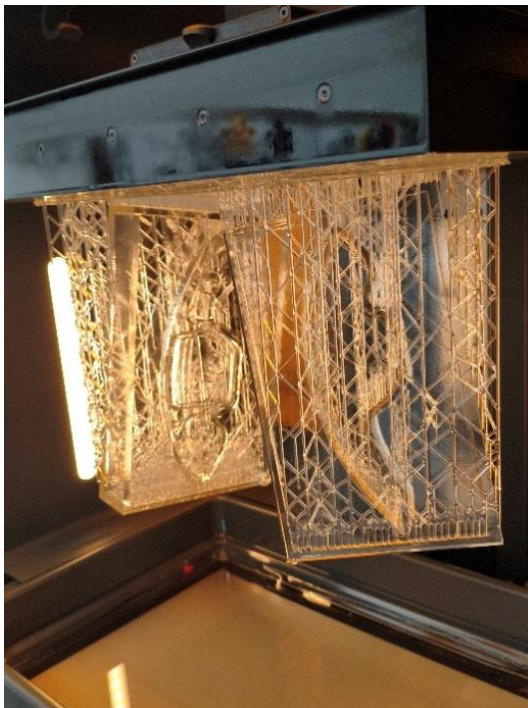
Molde de resina Clear Resin durante la impresión en la Form 3L.
